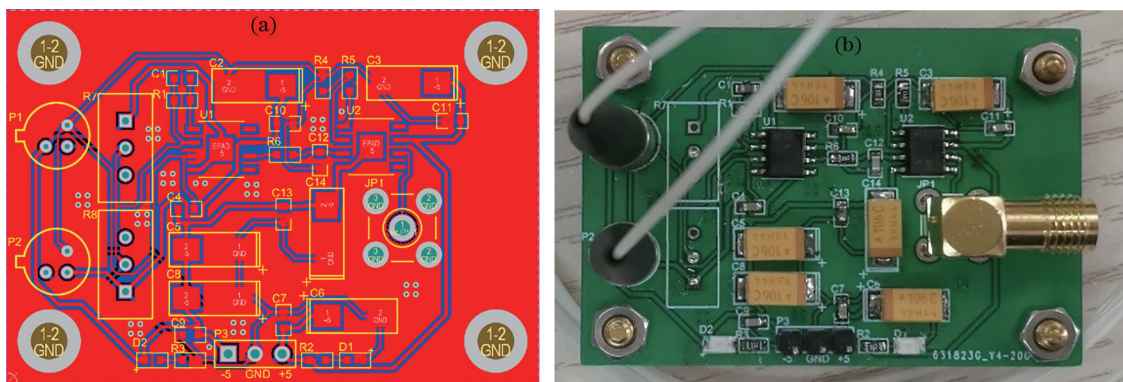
平衡光电探测器。(a) 电路 PCB; (b) 实物电路
